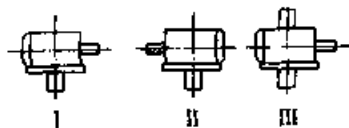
PWS 型减速器外形尺寸及装配型式
